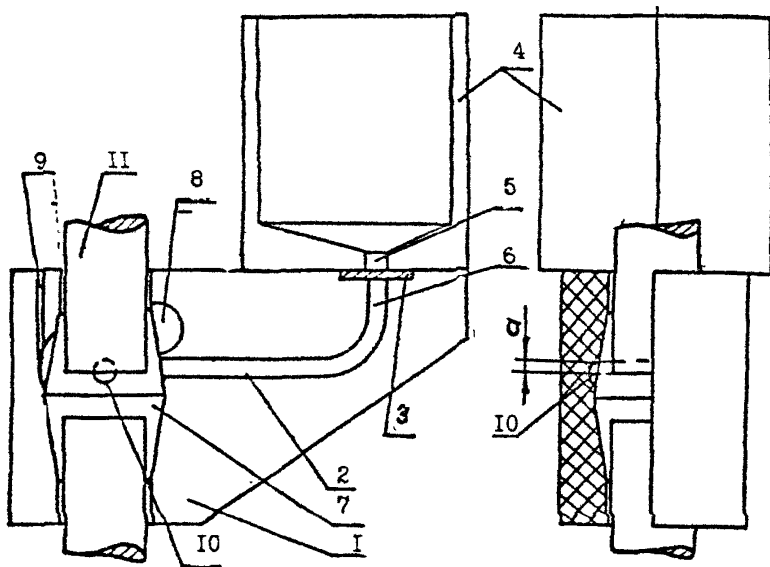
Сборка формы и тигля при сварке вертикального соединения стержней
